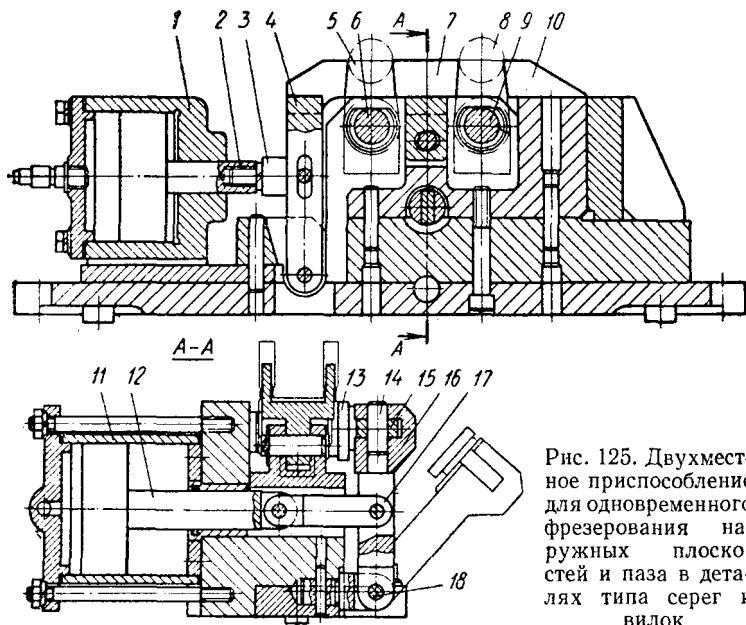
Двухместное приспособление для одновременного фрезерования наружных плоскостей и паза в деталях типа серег и вилок
